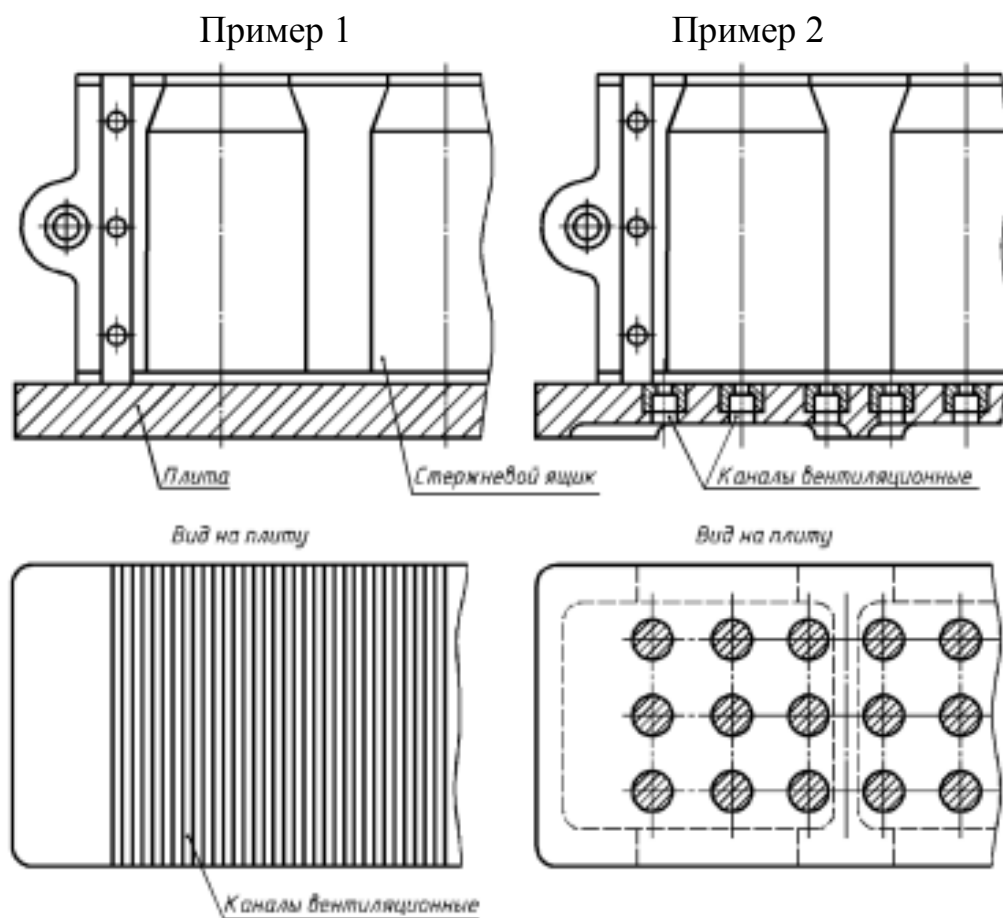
Примеры установки стержневого ящика на вентиляционную плиту
